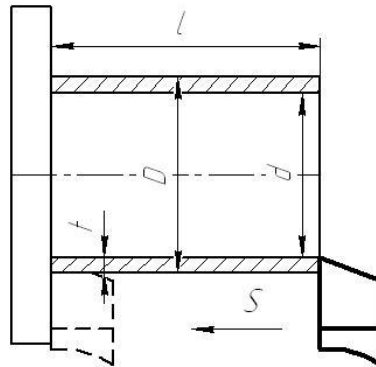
Обтачивание цилиндрической поверхности до уступа
